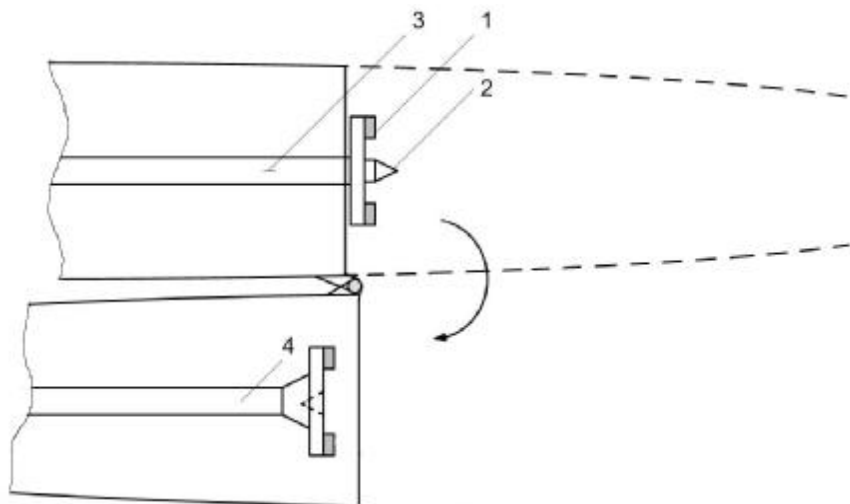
Схема расстыковки трансмиссионного вала на корабельных одновинтовых вертолетах (вид сверху).
